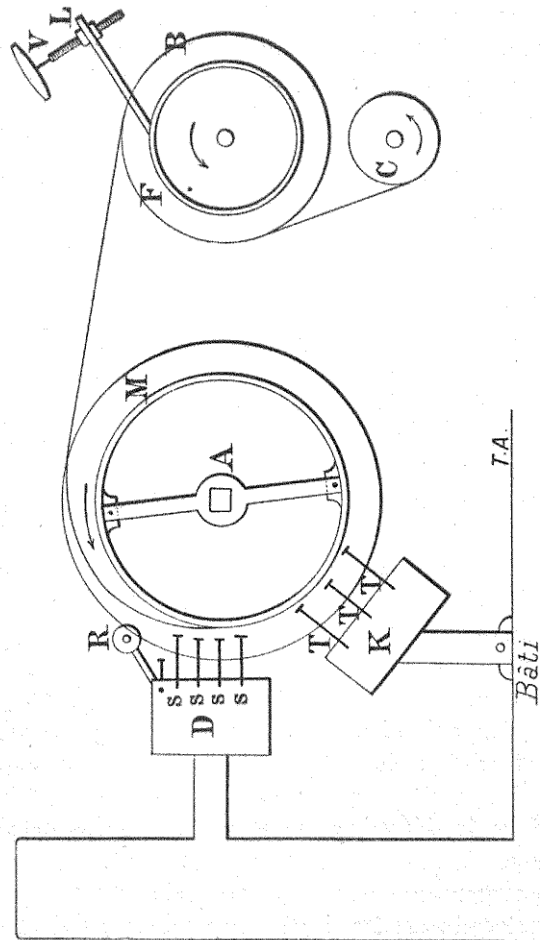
Machine à fabriquer les carcasses de pneus.
